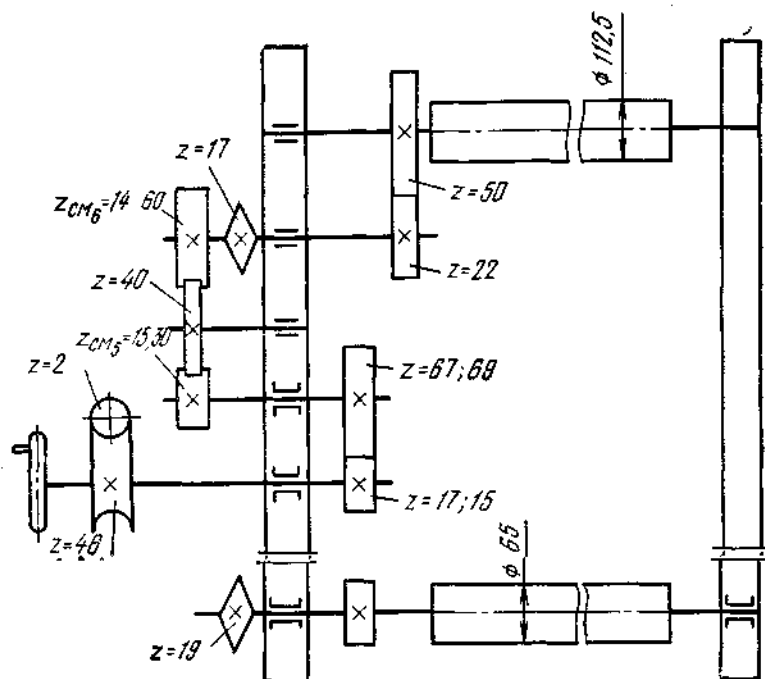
Кинематическая схема товарного регулятора станка АТПР-120-ЛМ
